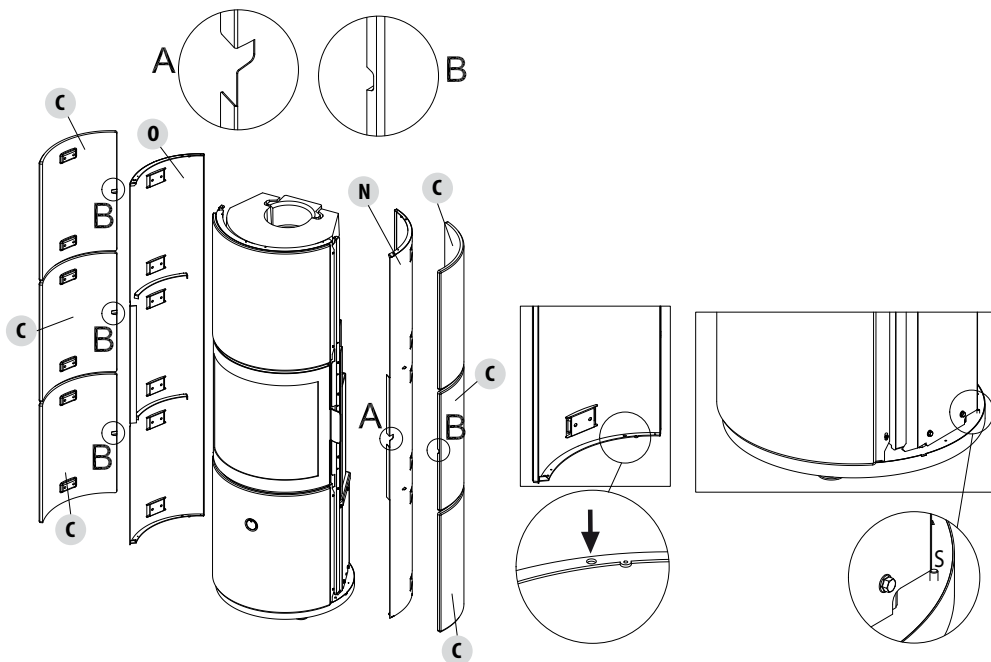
ASSEMBLAGGIO PANNELLI LATERALI
